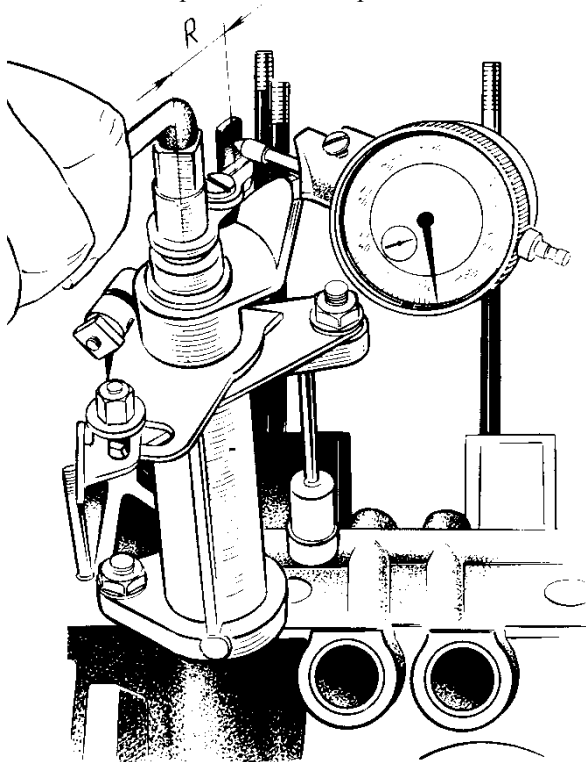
Проверка бокового зазора в зацеплении шестерни привода распределителя при помощи приспособления с индикатором
